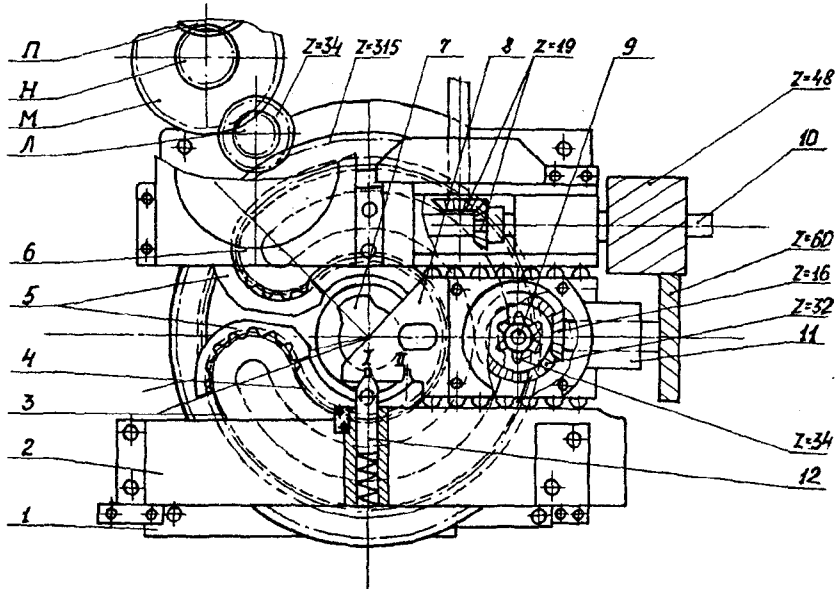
Схема реверсивного механизма с составным зубчатым колесом
